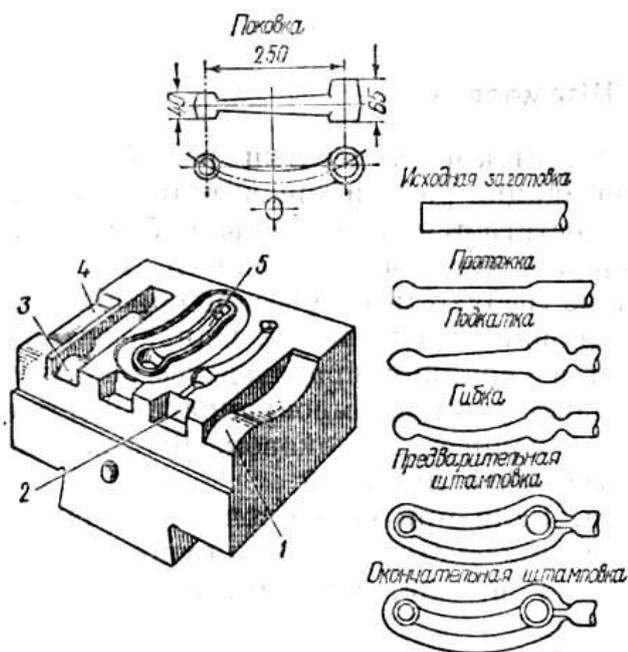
Схема многоручьевого штампа: 1-верхний штамп; 2-нижний штамп
